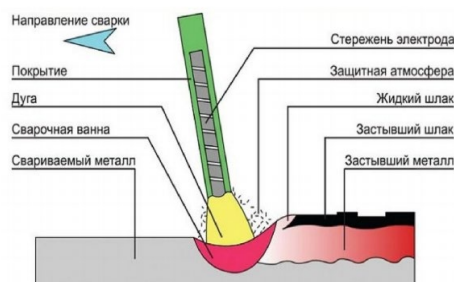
Схема ручной дуговой сварки покрытым электродом
